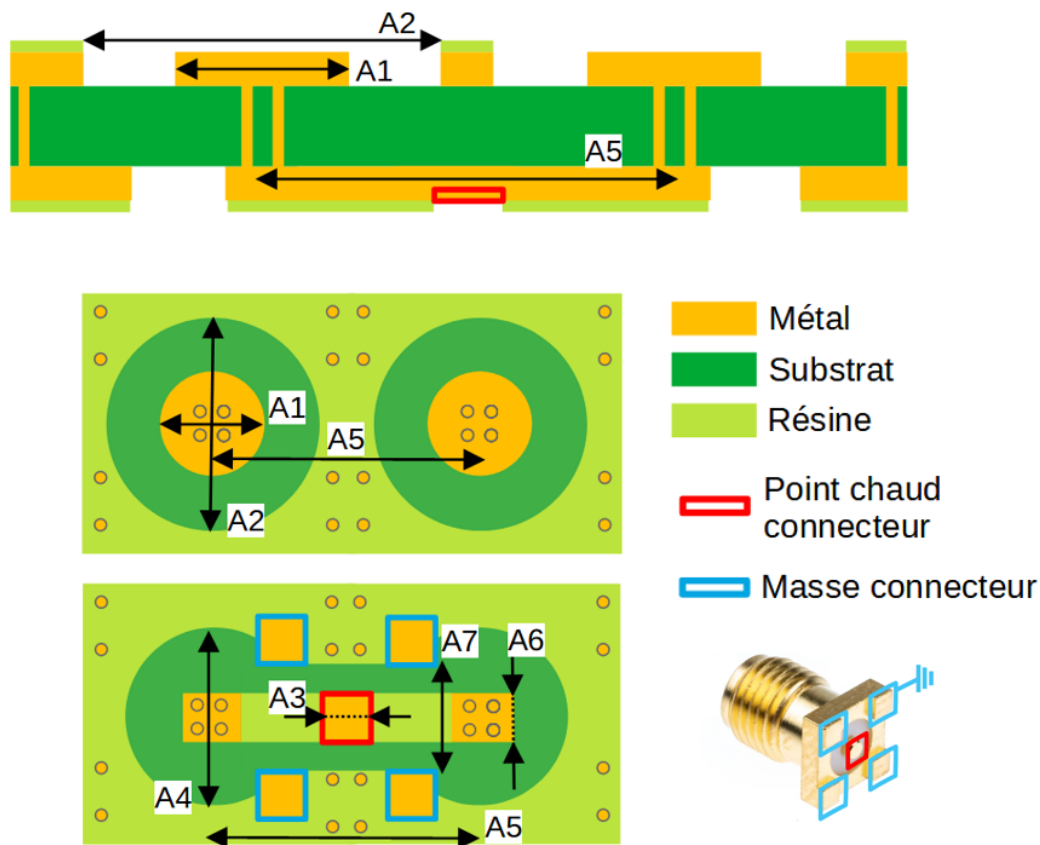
Schémas techniques d'un applicateur RF dit « doublet » et ses dimensions : en haut, vue en coupe ; en bas à gauche, vue de dessus ; en bas à droite, vue de dessous
